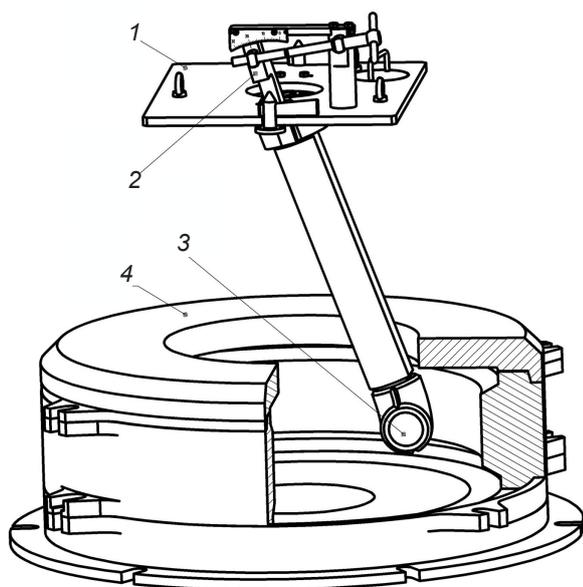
Поворотный желоб: 1 – неподвижная несущая плита; 2 – механизм угла поворота; 3 – поворотный узел протока металла; 4 – форма
